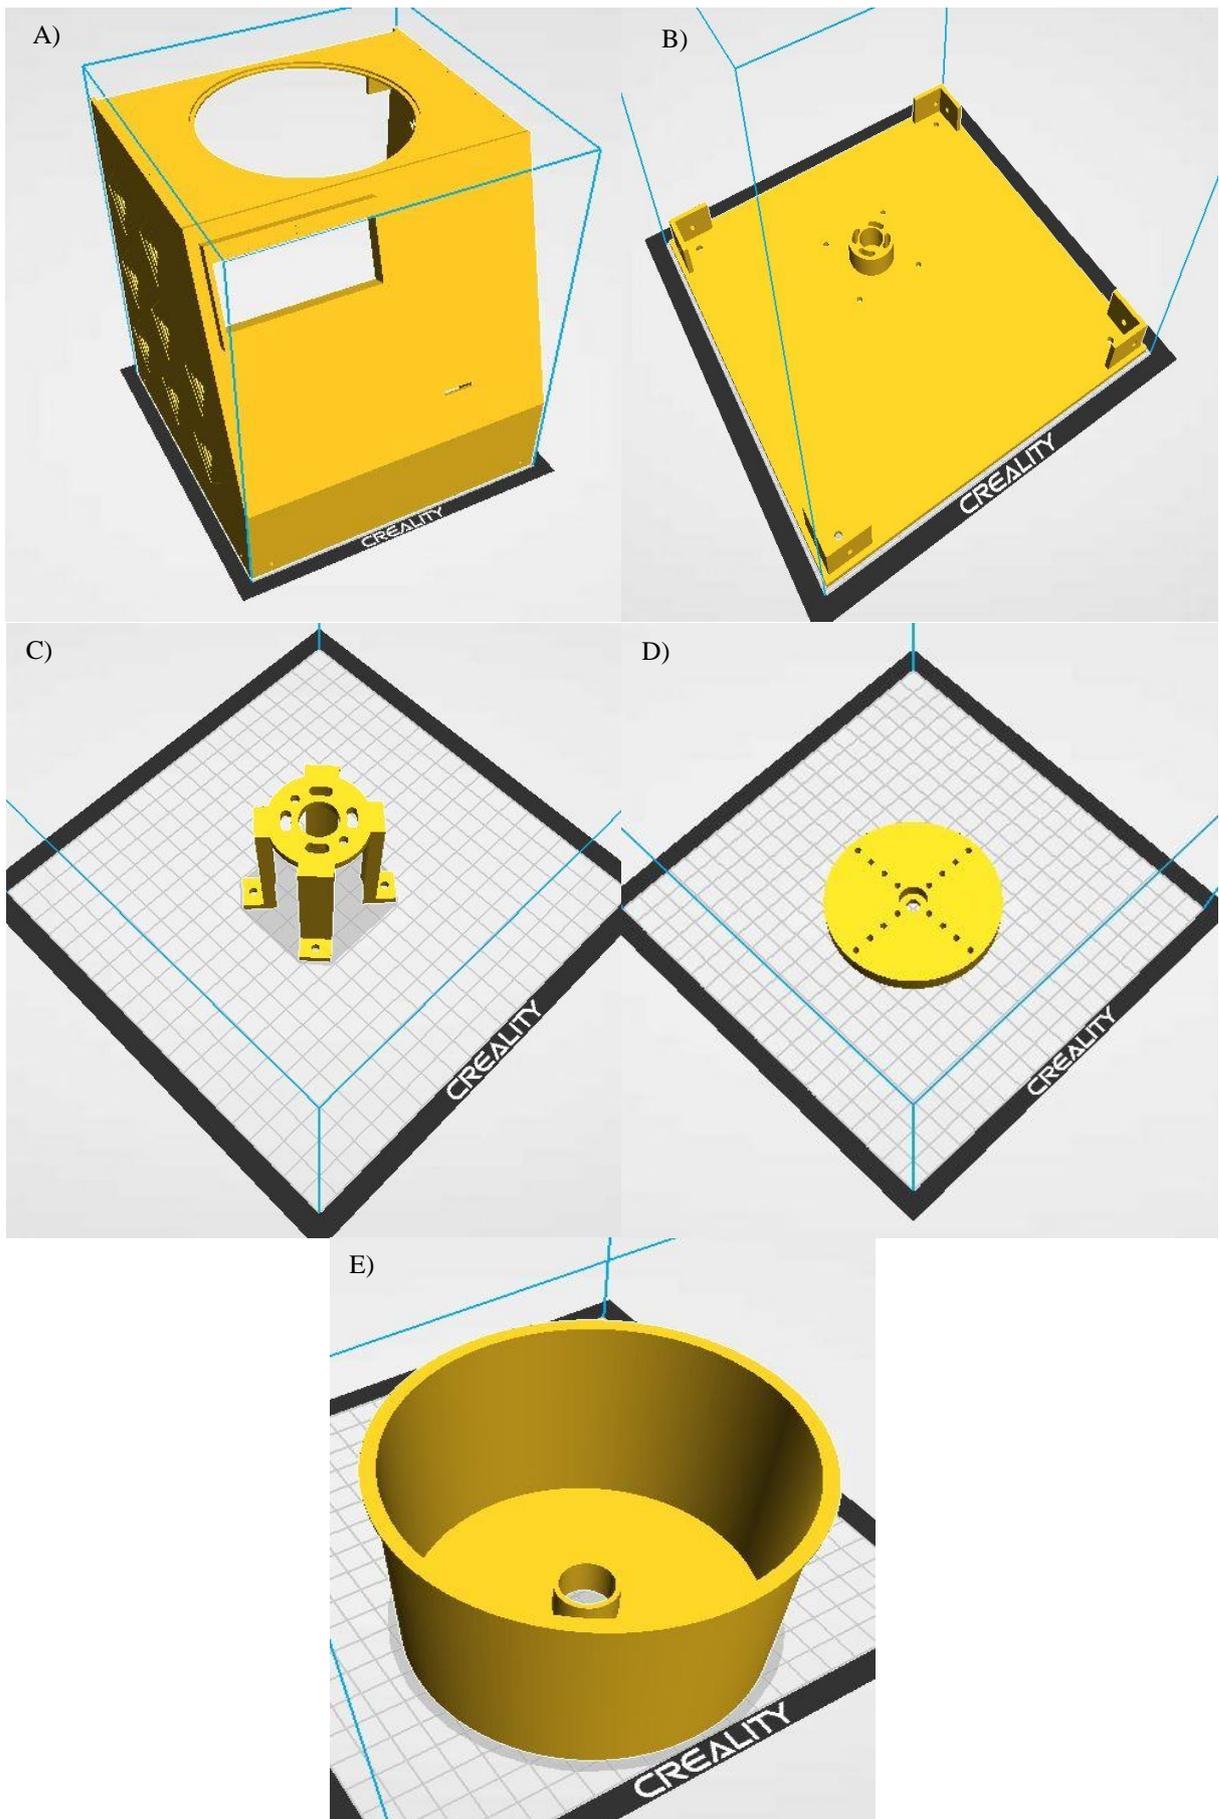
Vue 3D des pièces imprimables dans Crealty
